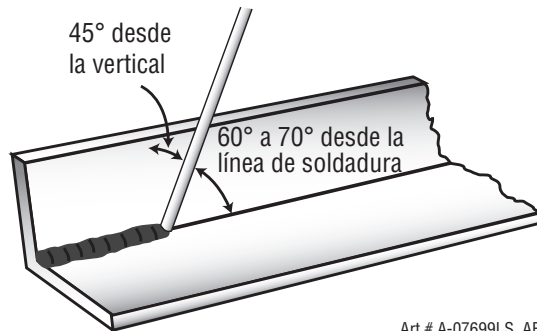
Posición del electrodo de la soldadura de perfil en ángulo HV
